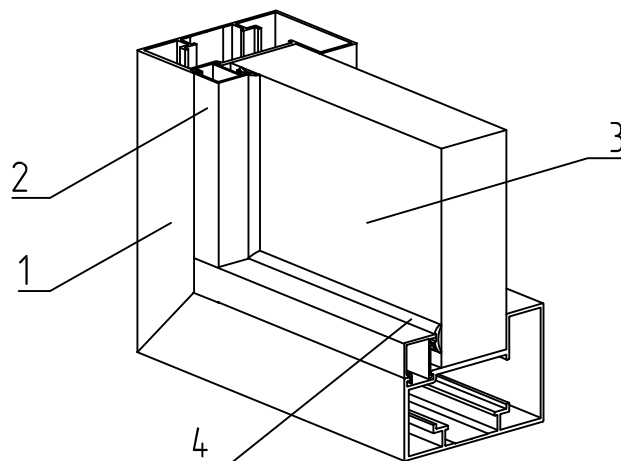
Установка штапика FLGU.400.0301 и уплотнителя FRK12 в створку откатных или распашных ворот Comfort
